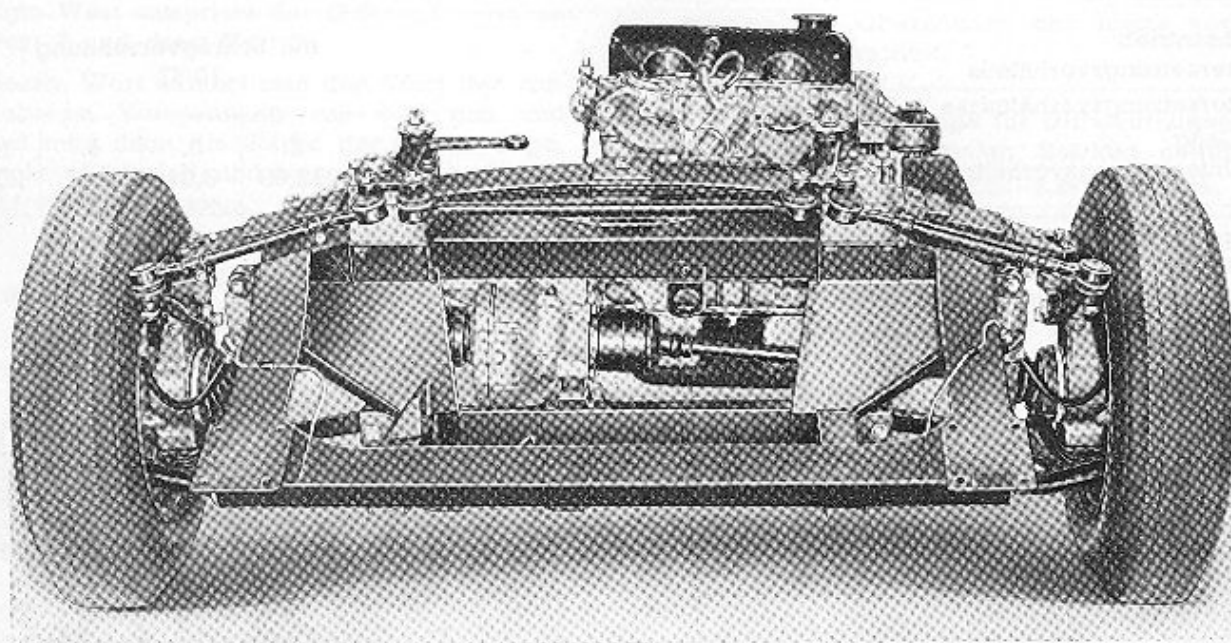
Ansicht der vorderen Radaufhängung und Motoraufhängung von der Rückseite.
